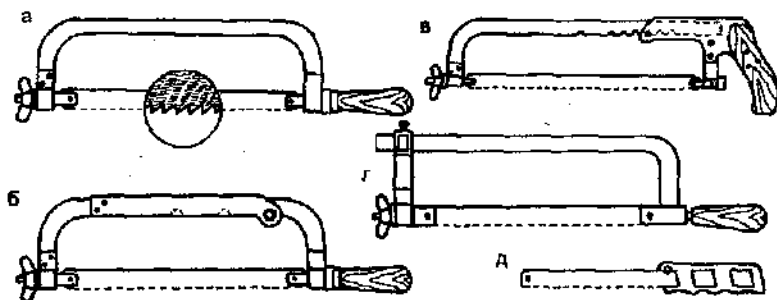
Ручная слесарная ножовка (станок): а — цельная; б — раздвижная; в — усовершенствованной конструкции; г — с передвижным держателем; д — для мелких работ и работы в стесненных условиях
